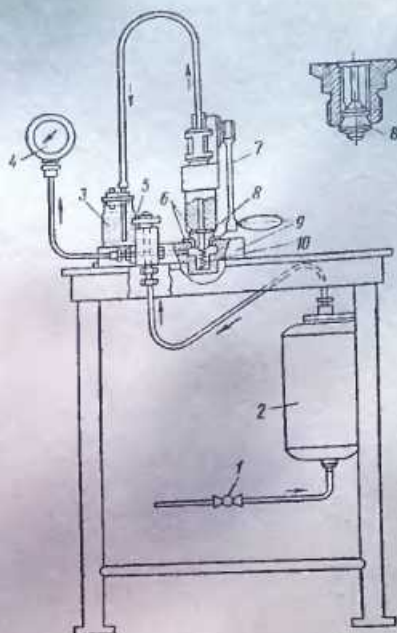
Схема установки ЛМ9690-198 для проверки герметичности нагнетательных клапанов топливного насоса: 1 — кран; 2 — ресивер; 3 — стеклянный сосуд; 4 — манометр; 5 — втулка подачи воздуха; 6 — прокладка; 7 — рукоятка; 8 — проверяемый нагнетательный клапан; 9 — корпус; 10 — пружина нагнетательного клапана
